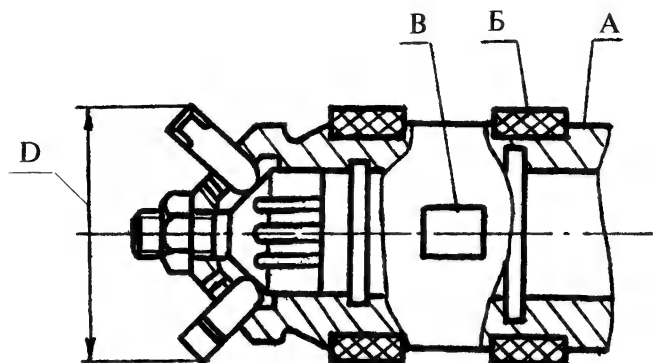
Комбинированная расточная головка: А - корпус, Б - шпонка, В - плавающая пластина
